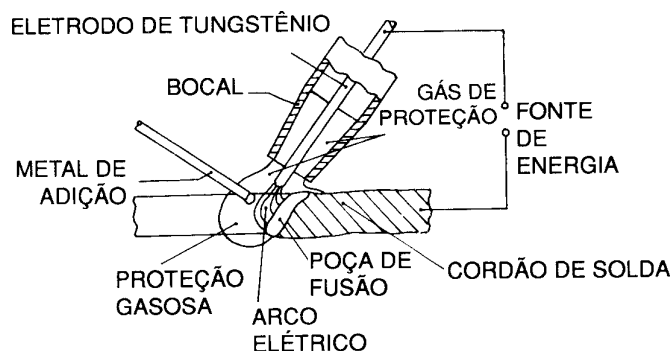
Processo de soldagem TIG (WAINER, 1995)
